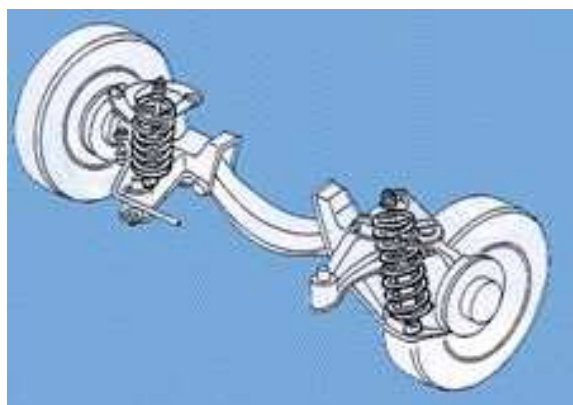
Zadní náprava vozu Smart Fortwo [9]
